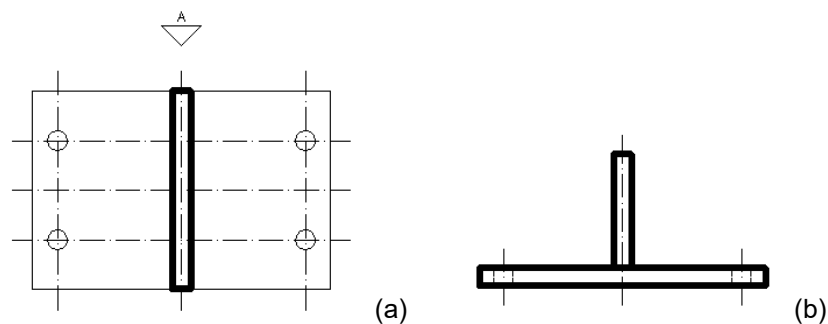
Detalhes do suporte para apoio direto na máquina de ensaio de tração. (a) Vista Superior e (b) Vista Lateral.
